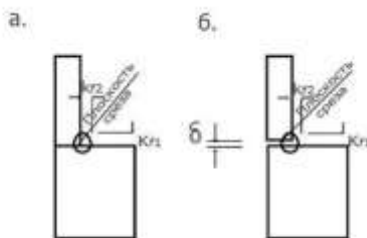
Сечения сварных швов в образцах, испытанных на отрыв без зазора (а) и с зазором (б)
